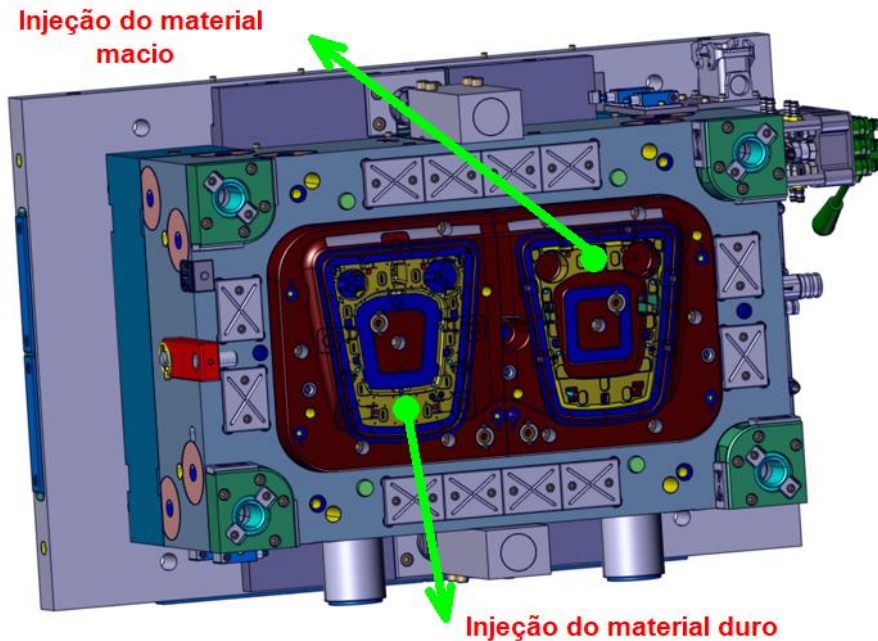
Exemplo de molde Bi-Material de transferência fabricado na SF Moldes.
